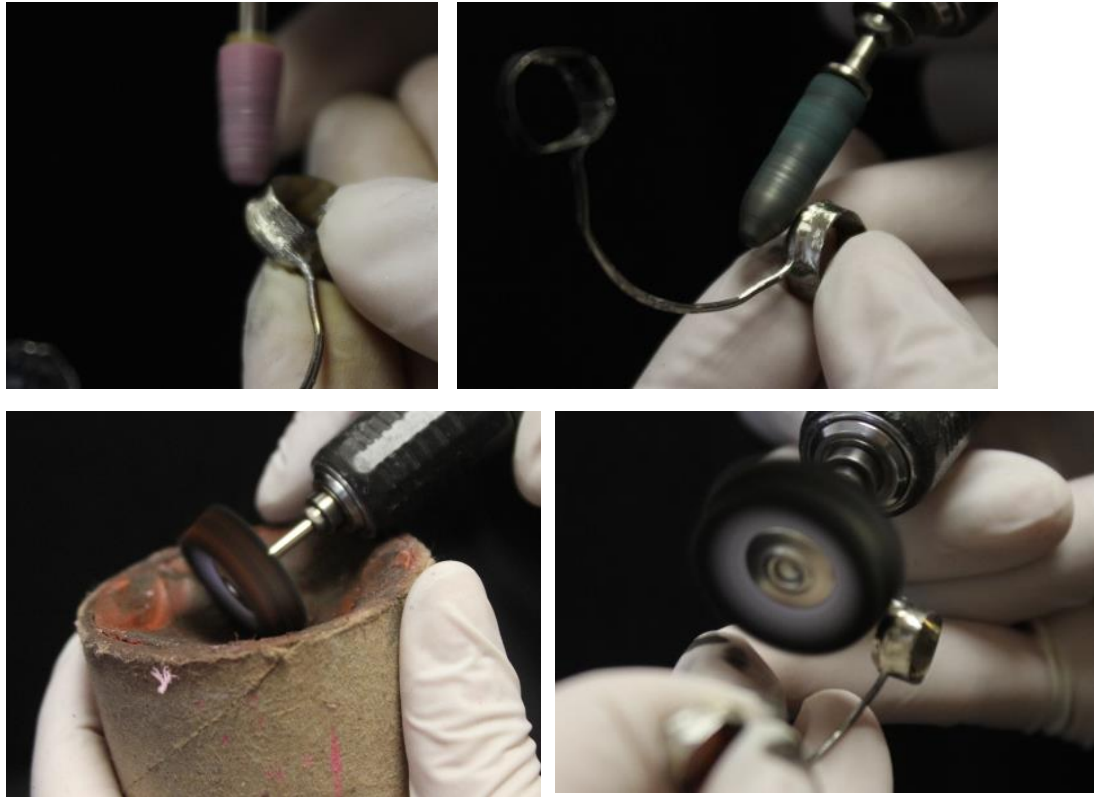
Recortado y pulido de las soldaduras. (Fuente propia)
